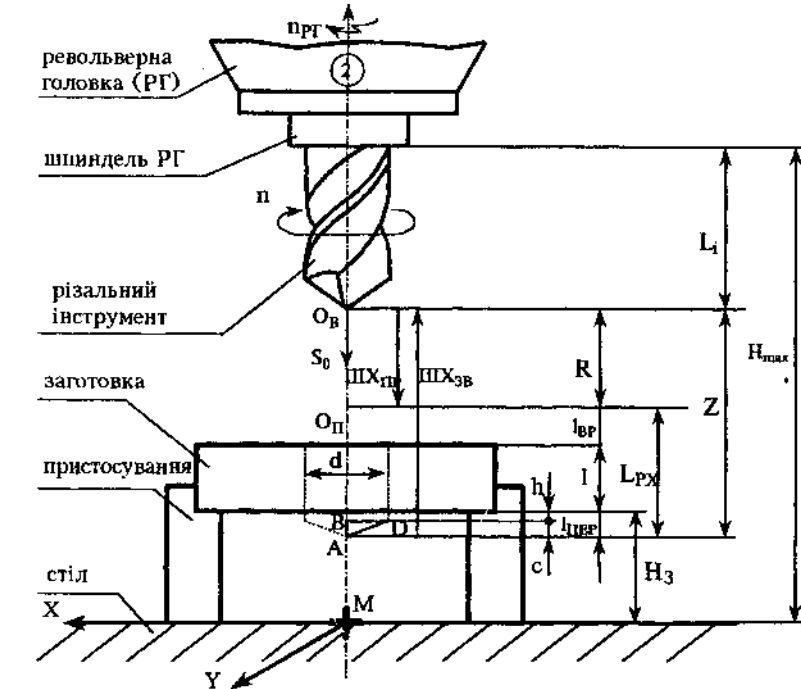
Схема взаємного розташування стержневого мірного інструменту (свердла) та заготовки при обробці отвору  $Od$
